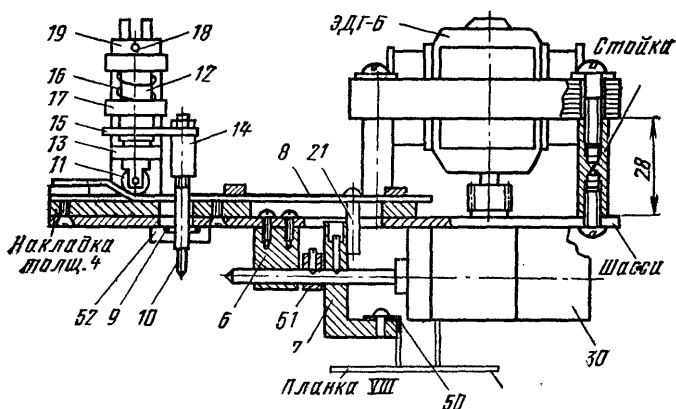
Конструктивная схема автоматического проигрывателя. Рим-П-ЭПУ-52. Стрелки указывают направление перемещения деталей.
